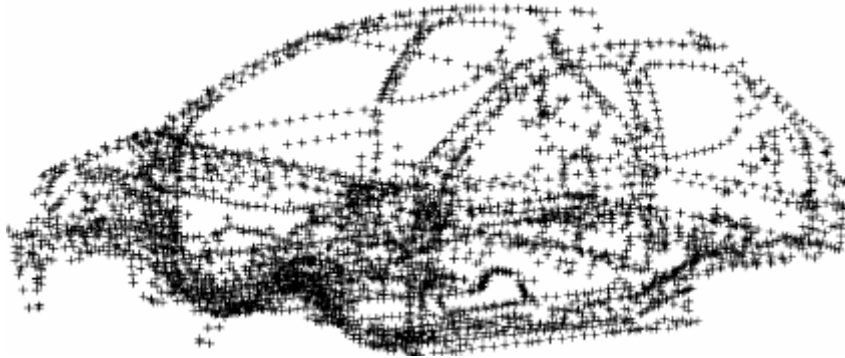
Position des points de soudure sur une caisse en blanc automobile [10]
